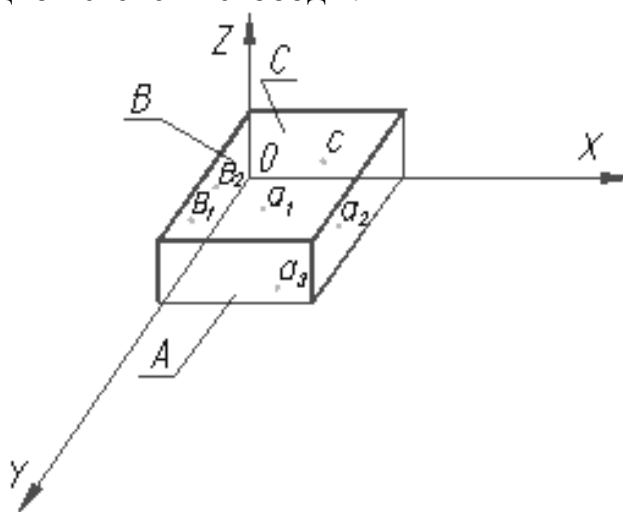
Схема расположения призматической заготовки в пространстве.
